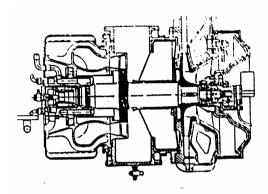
Общий вид турбокомпрессора с внешним расположением подшипников.
